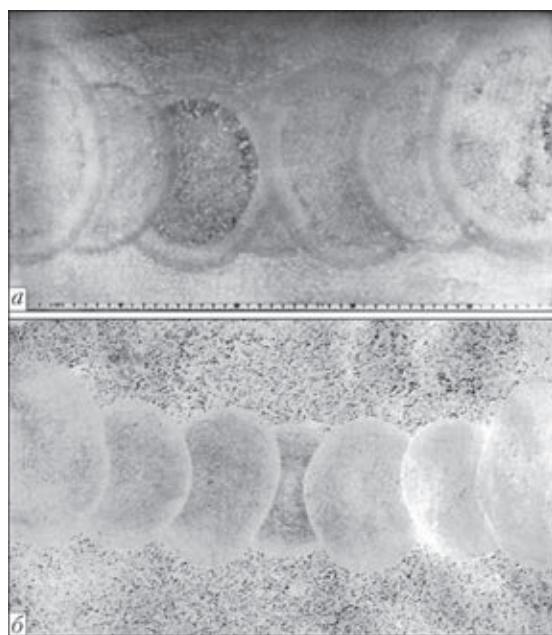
Поперечный макрошлиф (а) и серный отпечаток (б) сварного соединения толщиной 480 мм, выполненного новым способом
